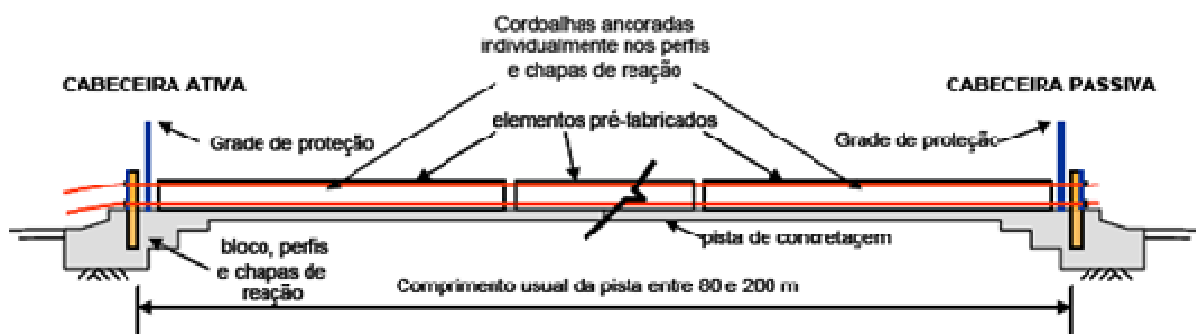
Esquema de fabricação de elementos pré-moldados em concreto protendido com aderência inicial. Fonte: Hanai (2005).
